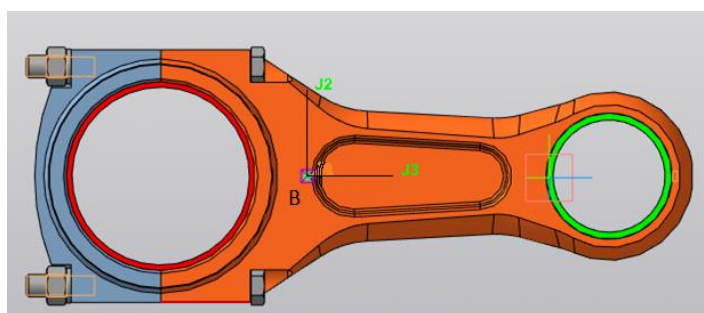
Кинематическая схема шатунно-крейцкопфного механизма.
